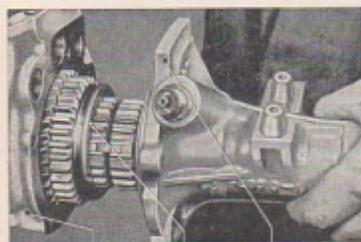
Getriebegehäuseverlängerung mit Hauptwellen-Zahnradblock aus Getriebegehäuse ausfahren
